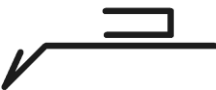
Пример условного обозначения лицевой стороны сварного шва.
